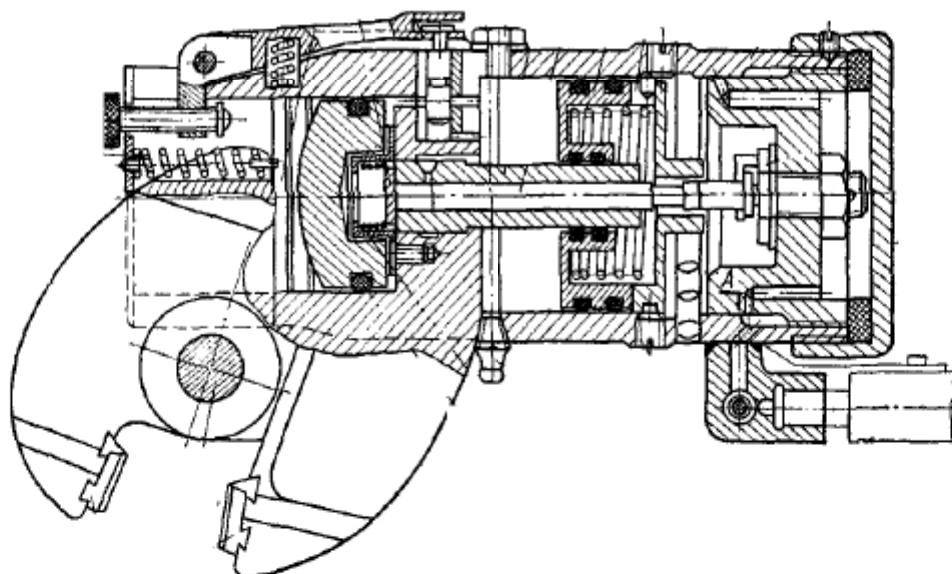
Гидравлическое приспособление для разрезания гаек
